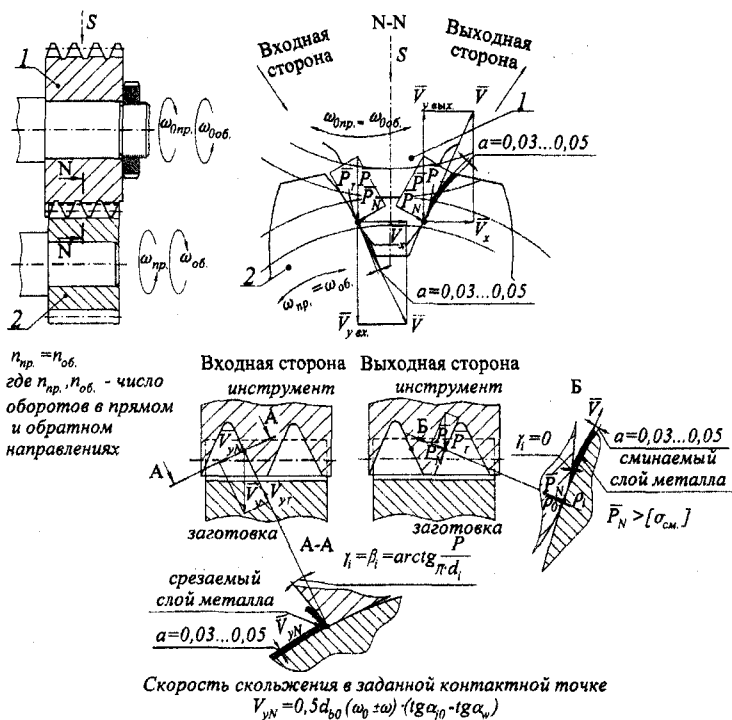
Схема шевингования –прикатывания цилиндрических зубчатых колес
